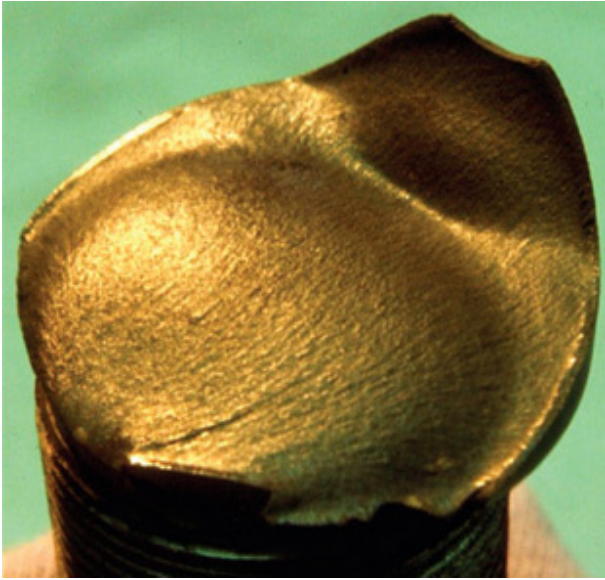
Хрупкий излом, показывающий «шеvronные следы» слева от шпоночной канавки, произошел, когда уронили ведущий вал большого редуктора.
